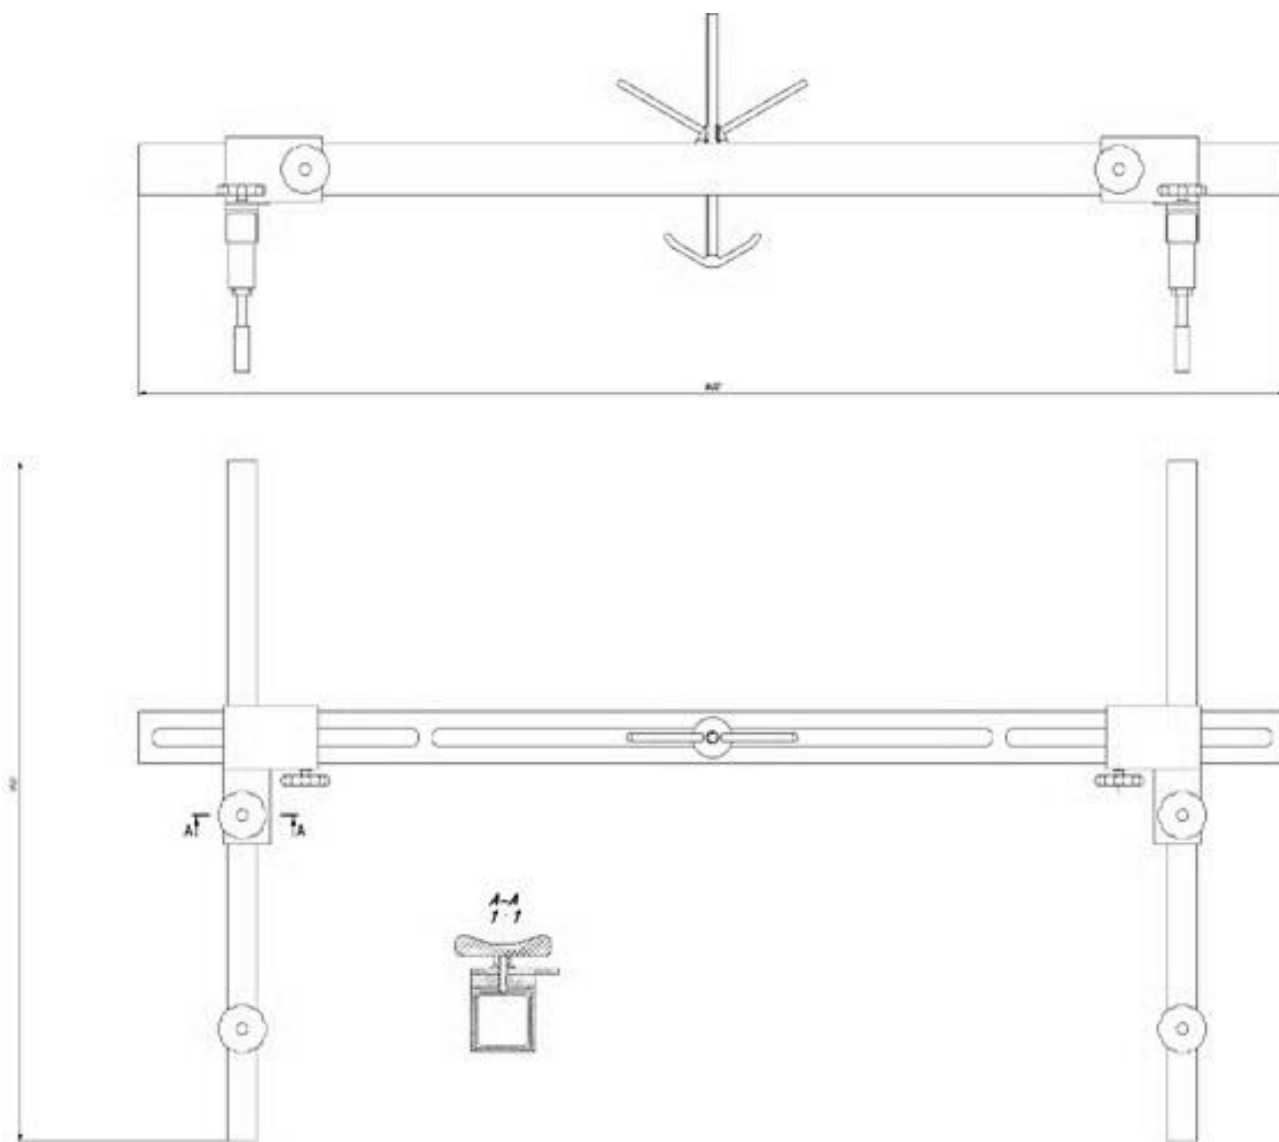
Эскиз сборочного чертежа (вид спереди и сверху)
